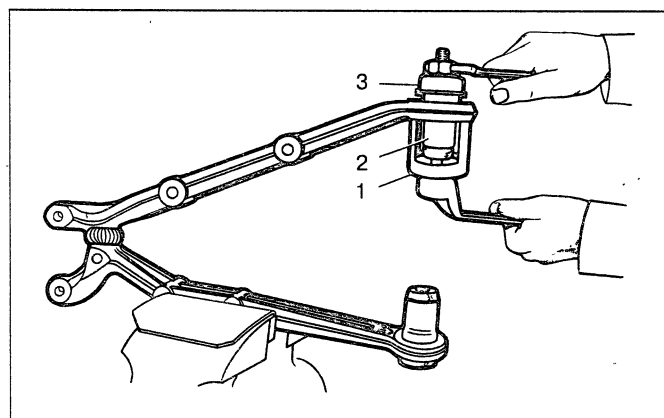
Запрессовка шарниров нижнего рычага: 1 – приспособление; 2 – шарнир; 3 – колпачок
